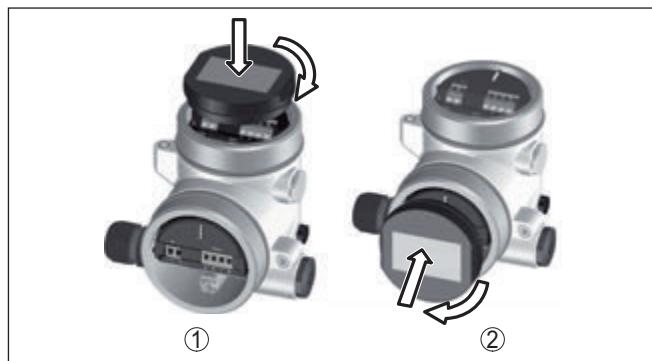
Установка модуля индикации и настройки в двухкамерном корпусе
